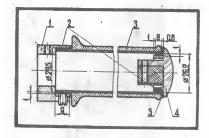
1— кольцо: 2— пластмассовые полоски; 3— трубка рукоятки газа; 4— грибок; 5— шайба.
